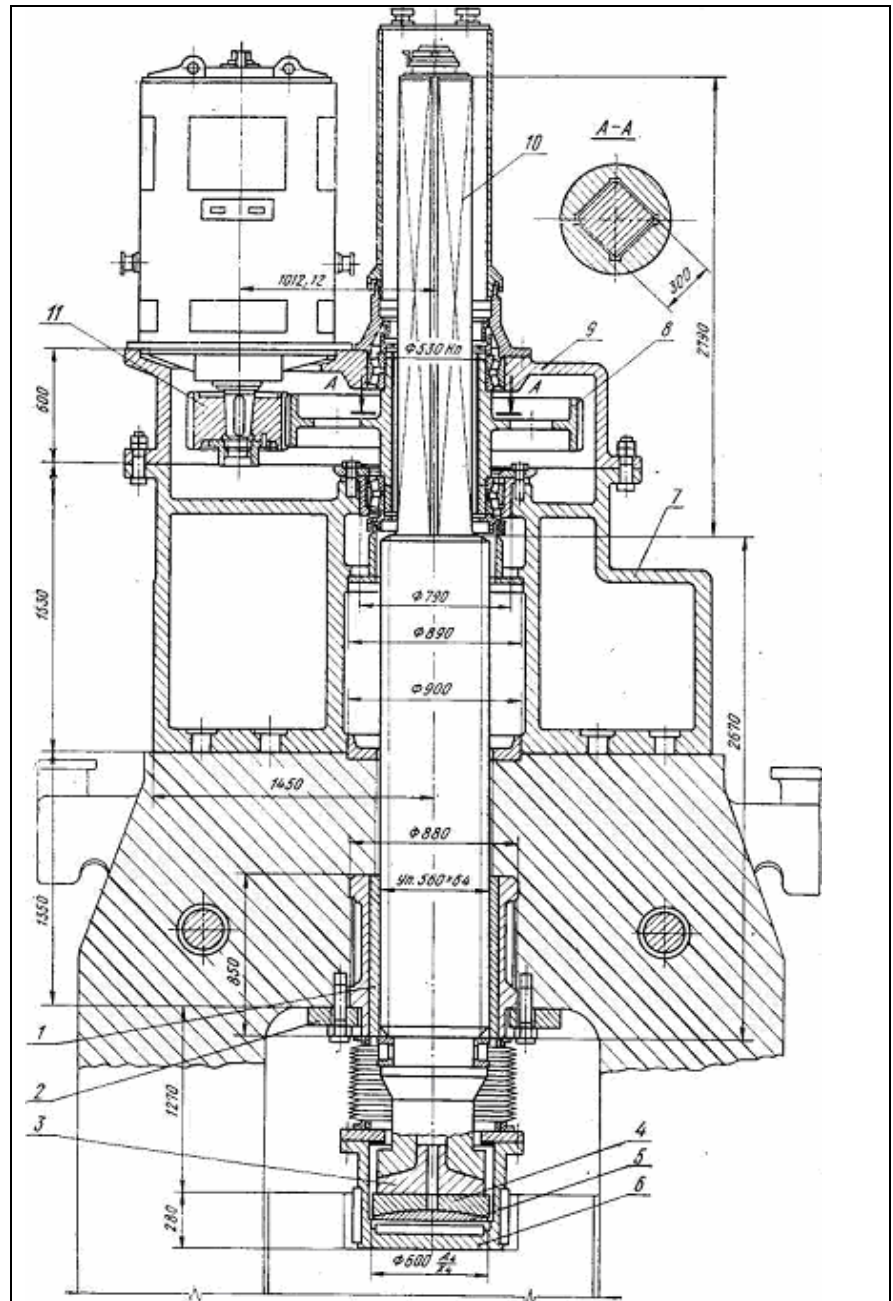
Быстроходный нажимной механизм блюминга 1500: 1 — нажимная гайка; 2 — планка стопорная; 3 — вкладыш; 4 — пята; 5 — подпятник; 6 — стакан; 7 — корпус; 8 — зубчатое колесо; 9 — крышка; 10 — нажимной винт; 11 — шестерня
